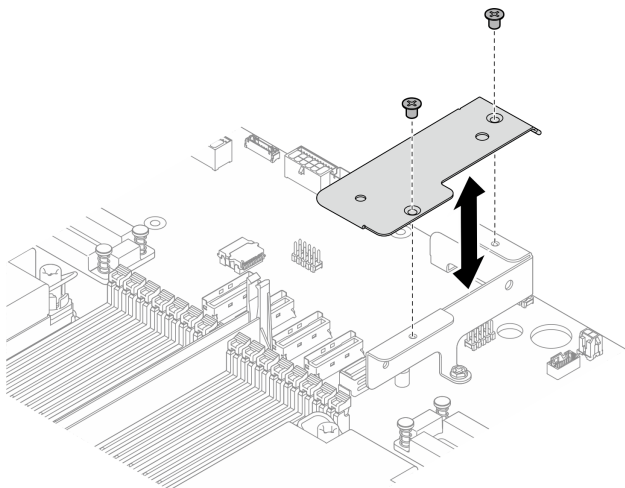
Entfernen der mittleren Kabelführungsabdeckung
